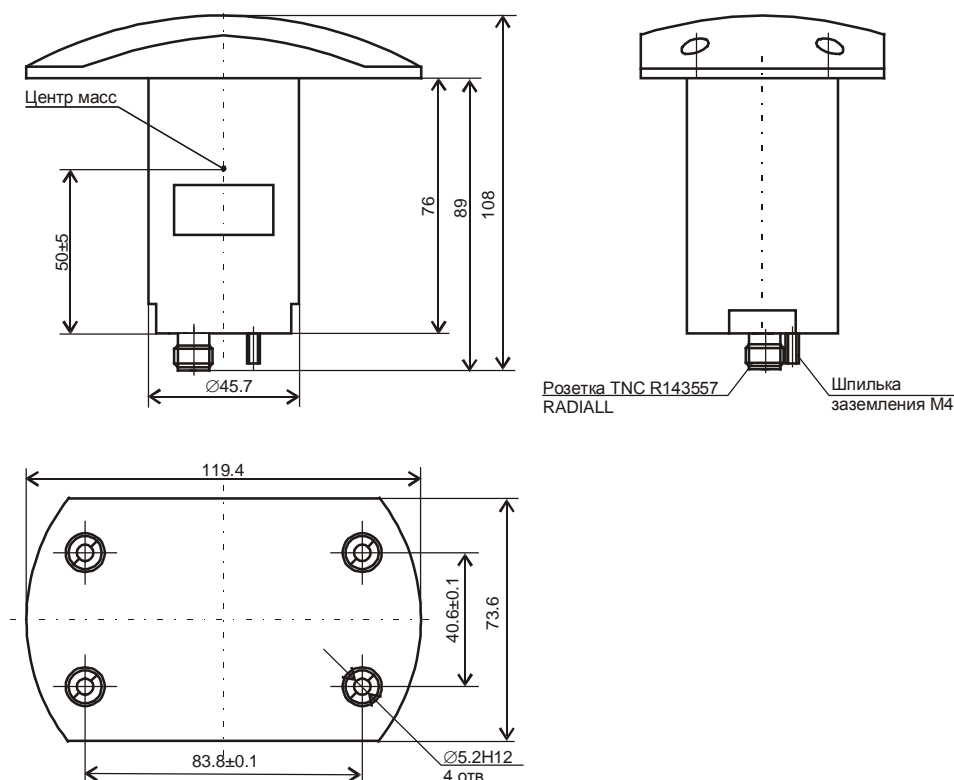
Внешний вид и габаритные размеры БА ПКАН.434854.030 и БА ПКАН.434854.011-03
